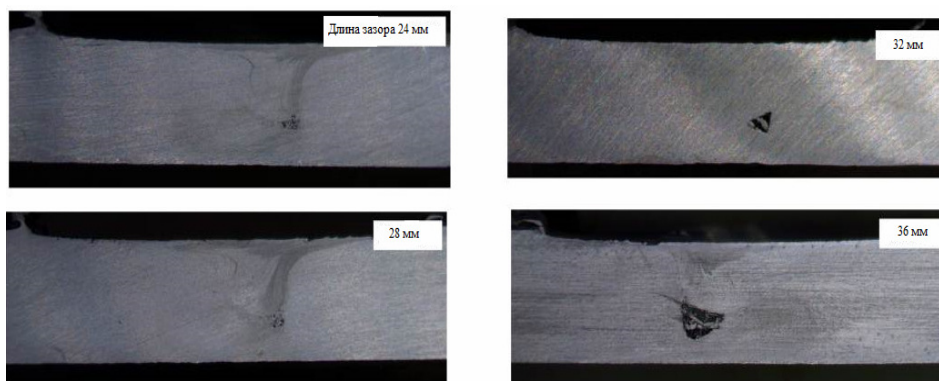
Макрошлифы образцов с зазором 2 мм с добавлением порошка
